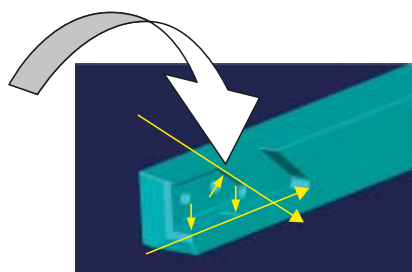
Der Wendeplattensitz im Halter gewährleistet mit seinem Innenanschlag die vollkommene Blockierung der Wendeplatte dank der entsprechenden Ausrichtung der beim Festziehen der Schrauben erzeugten Spannkräfte.
